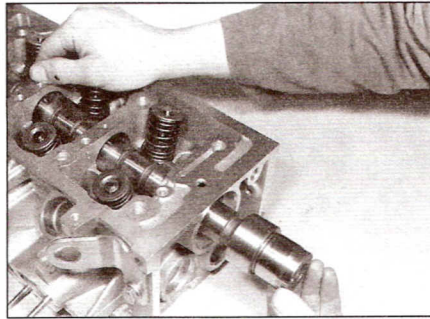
, б. ...затем вытяните распределительный вал из головки цилиндров (двигатели 1.4 л)
